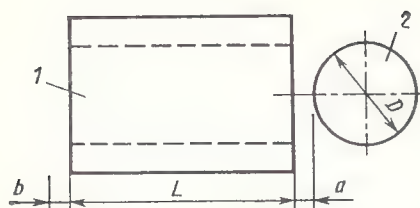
Расположение концевой или торцевой фрезы и детали:
